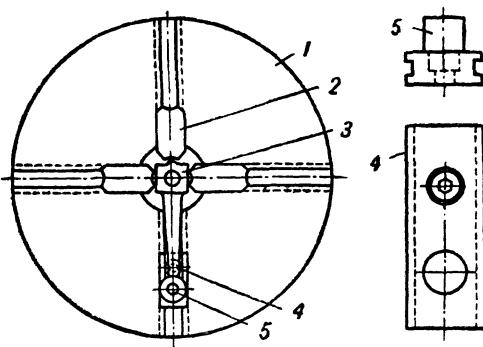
Четырехкулачковый патрон, приспособленный для расточки шатунов.
